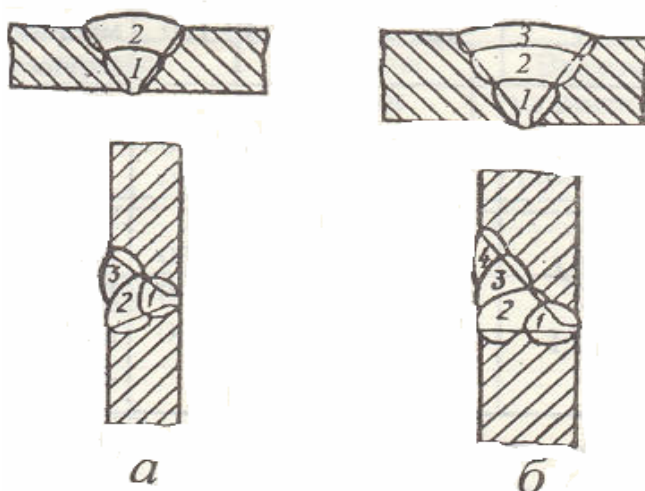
Порядок наложения слоев при сварке труб с различной толщиной стенки:
